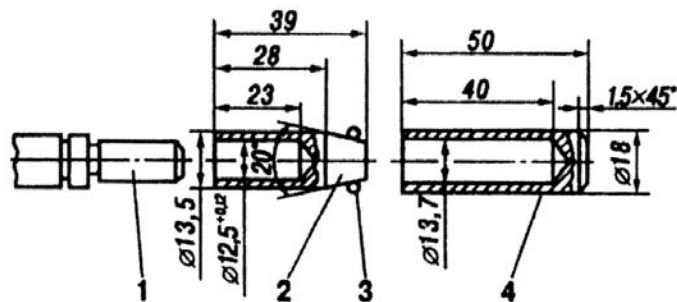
Приспособление для надевания пружинного кольца: 1 - вал якоря; 2 - направляющая втулка; 3 – пружинное кольцо; 4 - толкатель
